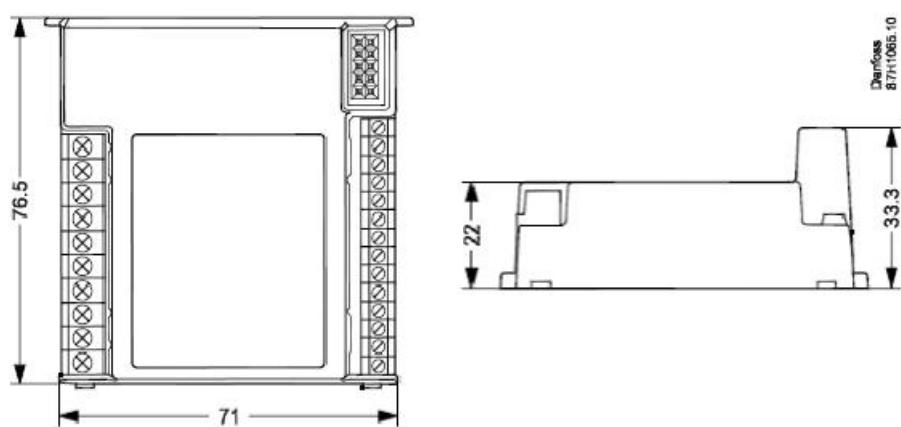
Габаритные и присоединительные размеры модуля ECA 32.
